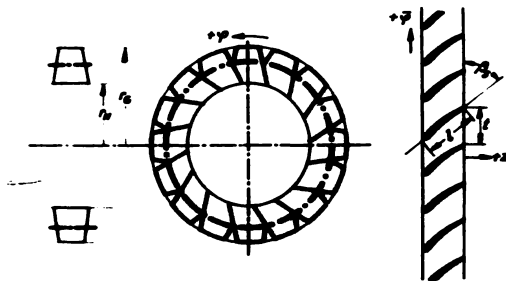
Secțiune coaxială printr-un rotor axial și desfiurarea ei pentru obținerea unei rețele drepte
